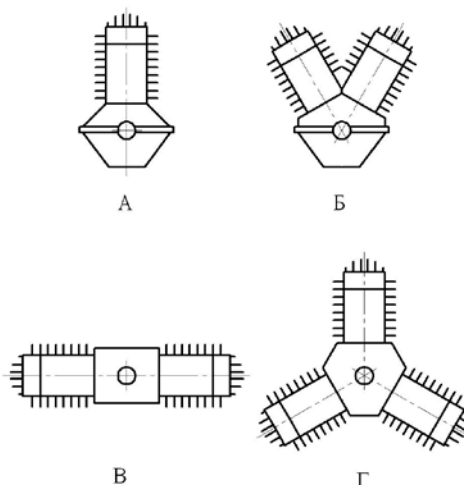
Схемы двигателей с различным расположением цилиндров:
